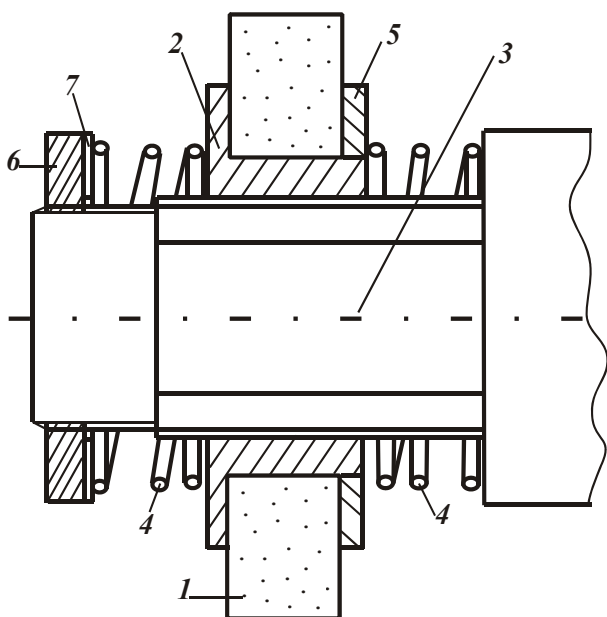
Схема крепления шлифовального круга с двухсторонним осевым перемещением: 1 – круг; 2 – шлицевая втулка; 3 – шлицевый вал; 4 – пружины; 5 – шайба или гайка; 6 – гайка; 7 – шайба.
